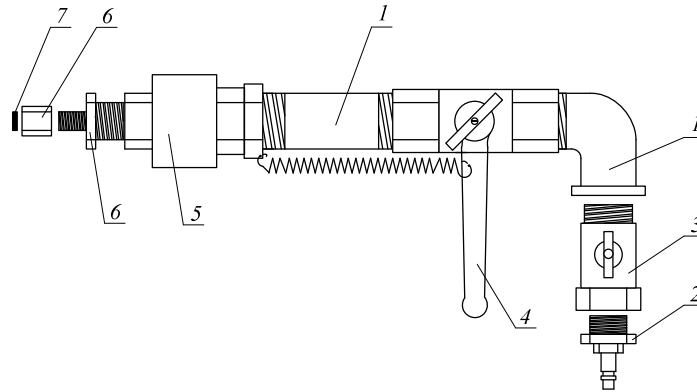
Пістолет-ін'єктор для ін'єкції та просочення стінових конструкцій ін'єкційними розчинами: 1 – корпус з трубок; 2 – вхідний штуцер; 3 – вхідний кран; 4 – ручка регулювання подавання ін'єкційного розчину; 5 – зворотний клапан; 6 – перехідник з накидною гайкою; 7 – ущільнювальна прокладка
